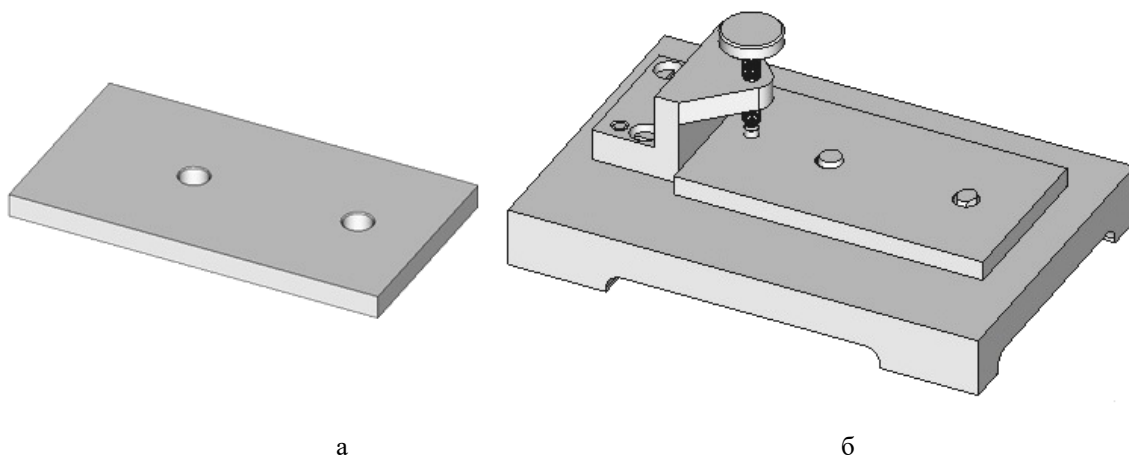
Установка заготовки «пластина» на пальцы:
